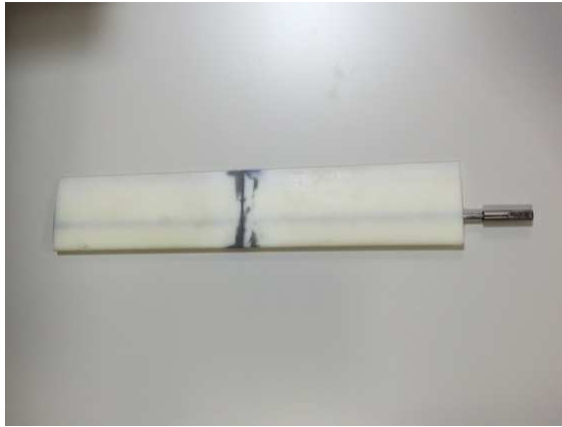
Perfil fabricado en el SAIT en dos piezas
